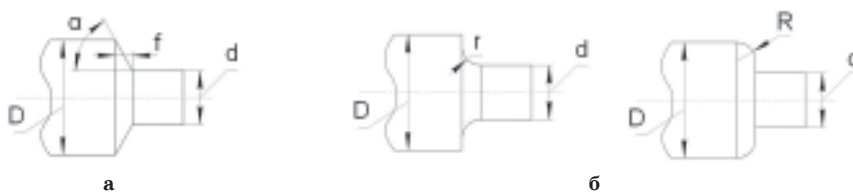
Конструктивні виконання насадок дозувального пристрою: а) із фаскою різної величини при основі насадки; б) із заокругленням при основі насадки
